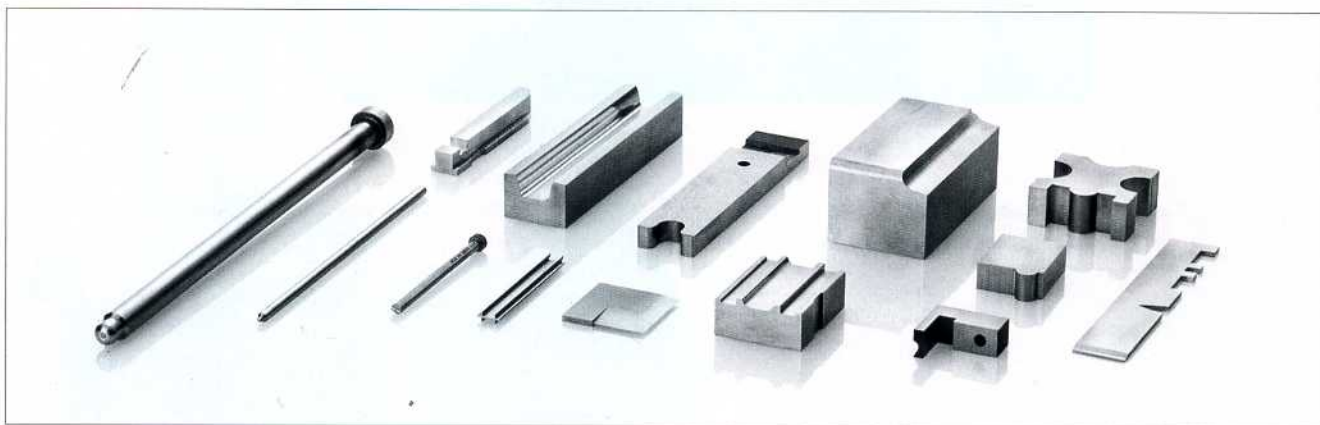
Der weltweit führende Systemlieferant in der Umform-, Schweiß- und Montagetechnik, Bihler, versorgt Kunden schnell und zuverlässig mit hochpräzise hergestellten Werkzeugen oder einbaufertigen Ersatzteilen. Dabei handelt es sich meist um kleine Teile, die als Stanz- und Biegewerkzeuge in den Maschinen und Automaten zum Einsatz kommen
